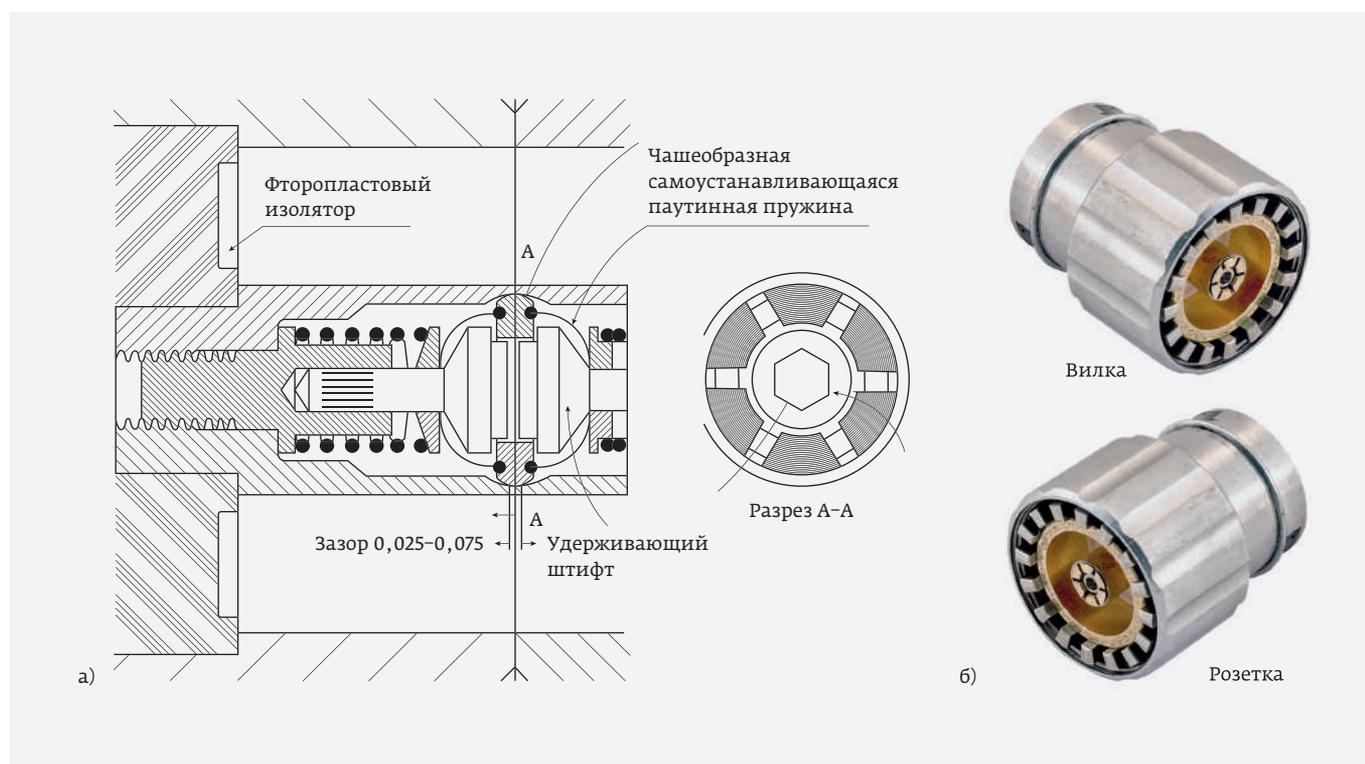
Конструкция (а) и внешний вид соединителя GR900 (14 mm)
